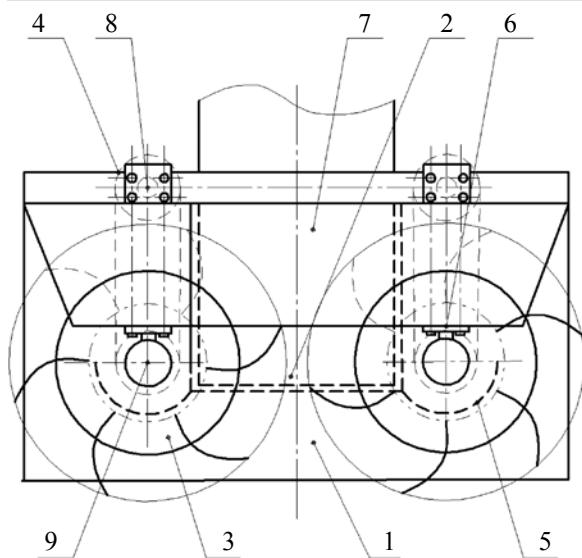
Схема лопастного питателя (вид сверху): 1 – наклонный лоток; 2 – выгрузное окно; 3 – ротор; 4 – механизм привода роторов; 5 – сектор; 6 – навесная коробка; 7 – передний брус; 8 – механизм привода; 9 – подшипниковые узлы
